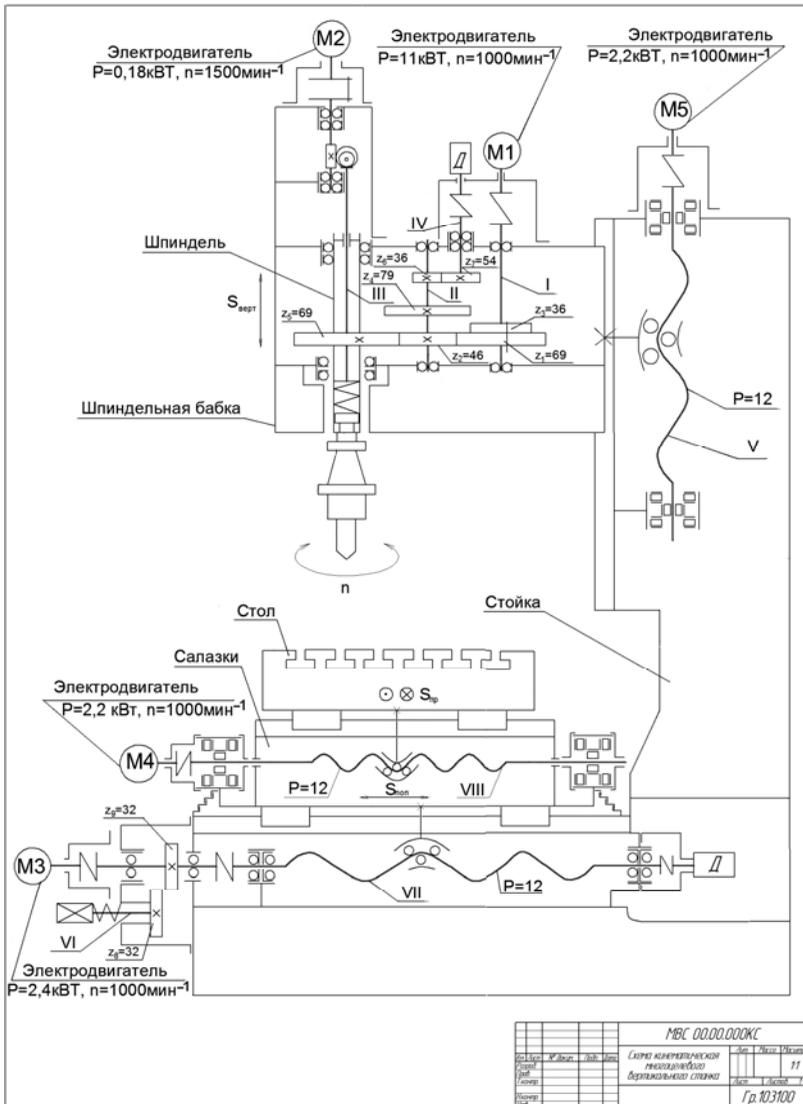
Кинематическая схема вертикального многооперационного сверльно-фрезерно-расточного станка с ЧПУ с приводами подачи шпиндельной бабки, стола и салазок
